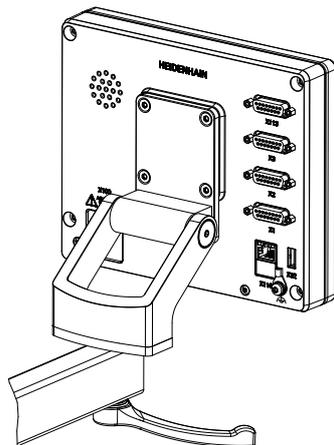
Монтаж устройства на креплении Multi-Pos
